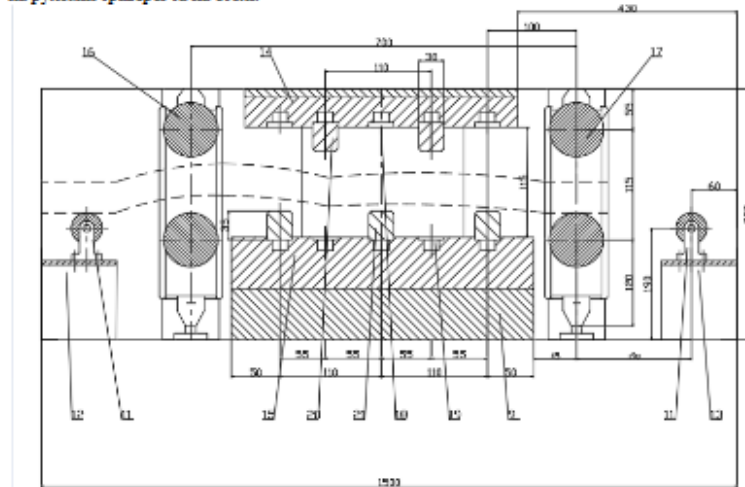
Конструкція пресу: 9 – стіл; 11 – приводні роликки; 12, 13 – піднімальні кріплення; 14 – верхня робоча плита; 15 – нижня робоча плита; 16, 17 – прокатні роликки; 18, 19 – напрямні пази; 20, 21 – інструментальні болти
